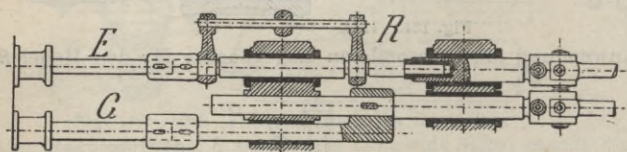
Die Kr öpfung der Grundschieberstange in dieser Ausführung mag für geringen Druck und nicht zu grosse Maschinen gestattet sein.
